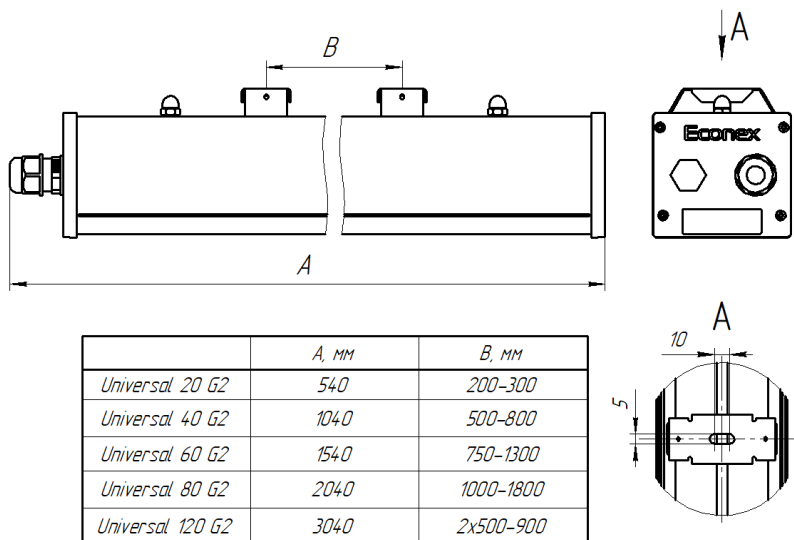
Габаритный чертеж светильника Econex Universal G2
